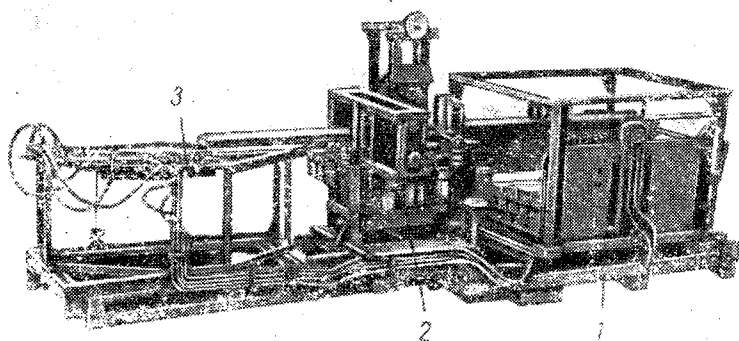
Полуавтоматическая линия для подачи шпал в наколочный станок ЦНИИС и уборки их из него
